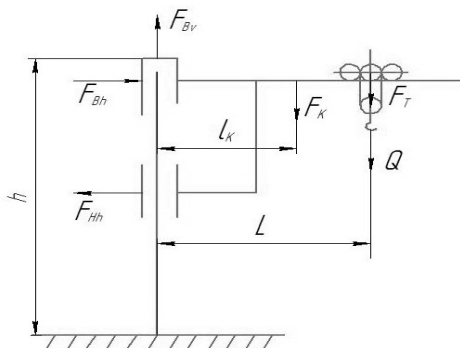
Расчетная схема консольно-поворотного крана на неподвижной колонне
